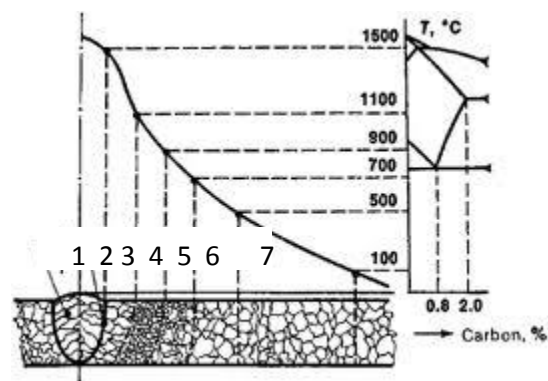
Esquema de las zonas desarrolladas en una soldadura
